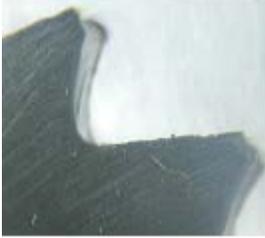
Устойчивость быстрорежущих дисковых фрез с различной обработкой
